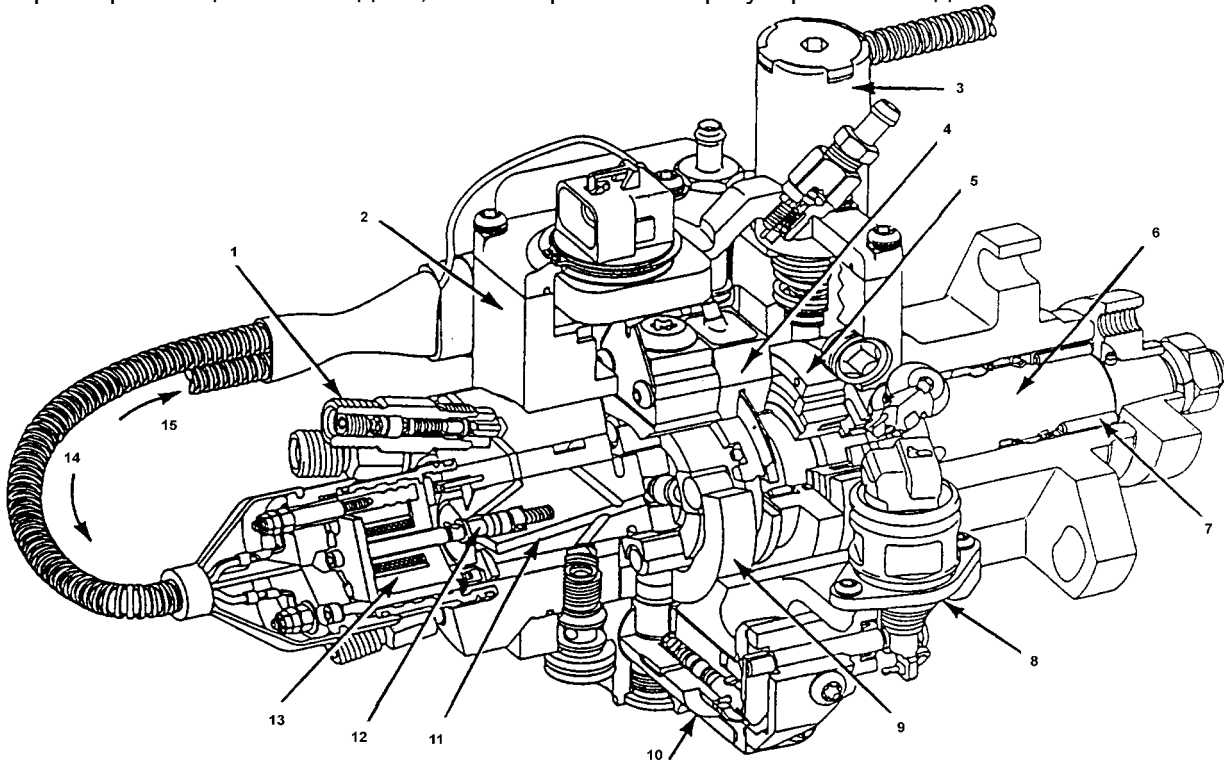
Роторный ТНВД DS Stanadyne: 1 - выпускной штуцер; 2 - корпус; 3 - выключатель ТП; 4 - оптический датчик положения вала; 5 - ТПН; 6 - вал; 7 - игольчатый подшипник; 8 - шаговый электродвигатель УОВТ; 9 - кулачковая шайба; 10 - следящий гидроривод УОВТ; 11 - ротор; 12 - управляющий золотниковый электроклапан; 13 - электромагнит; 14 - от установленного на ТНВД электронного блока; 15 - от центрального блока управления.
